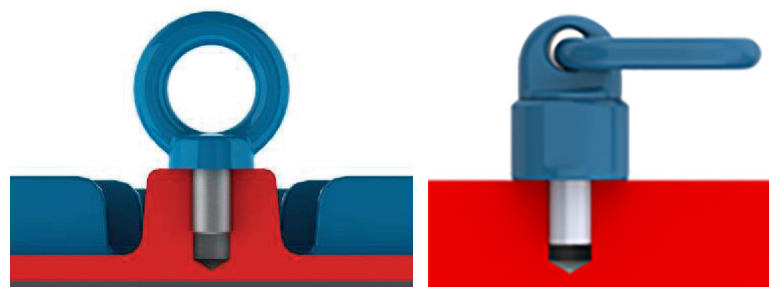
Korrekte Befestigung der Ringschraube
